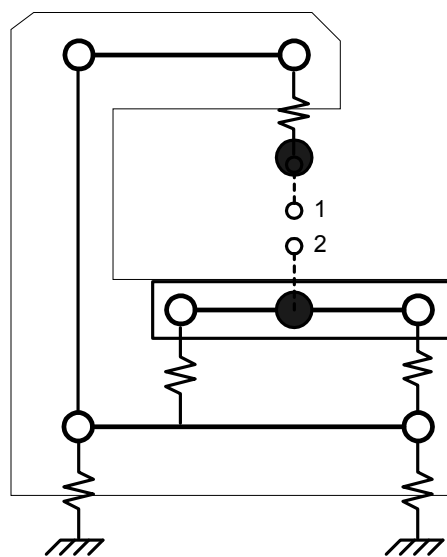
Розрахункова схема несучої системи вертикально - фрезерного верстата
